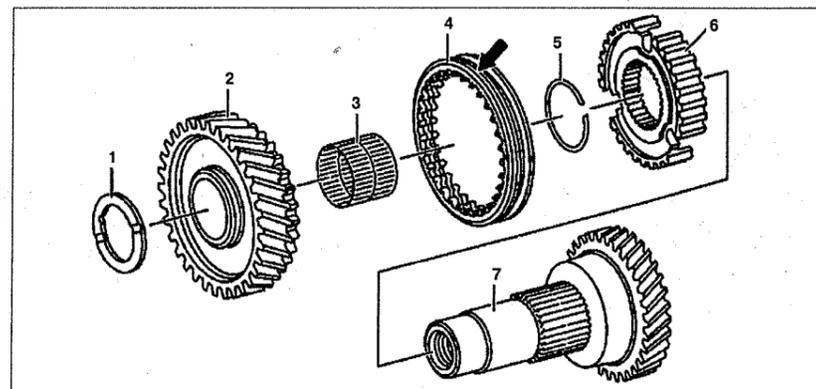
Вал передачи заднего хода (автомобили с двигателями 111.948 и 601.970): 1. Стопорная прокладка, 2. Шестерня заднего хода, 3. Игольчатый подшипник, 4. Скользящая втулка, 5. Стопорное кольцо, 6. Корпус синхронизатора, 7. Вал.
